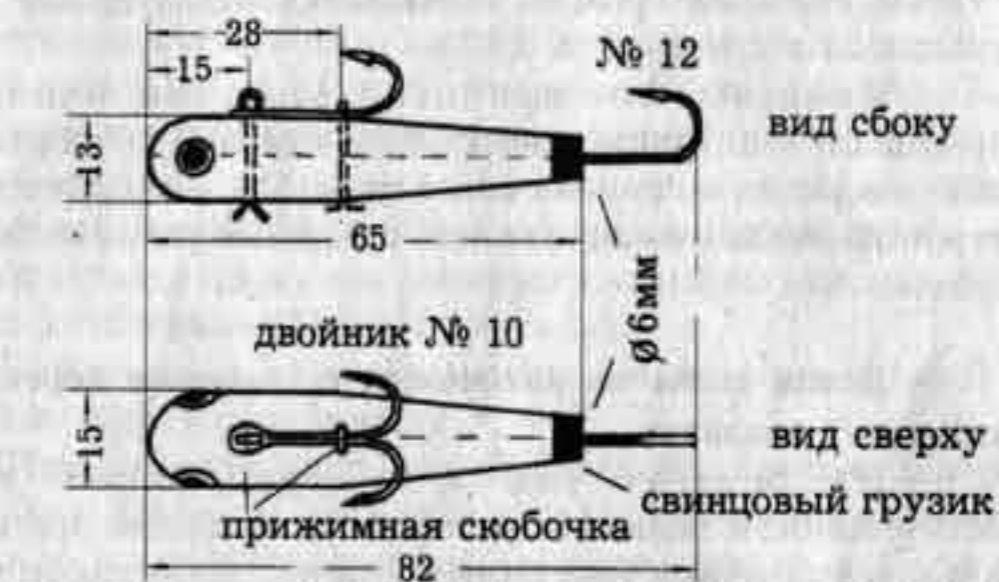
Пенопластовая рыбка для поплавка с кормушкой
